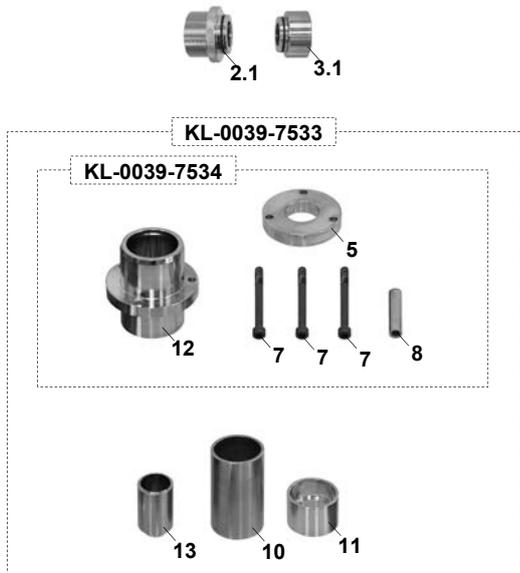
KL-0039-7531 - Jeu de douilles, Sprinter (W906)
